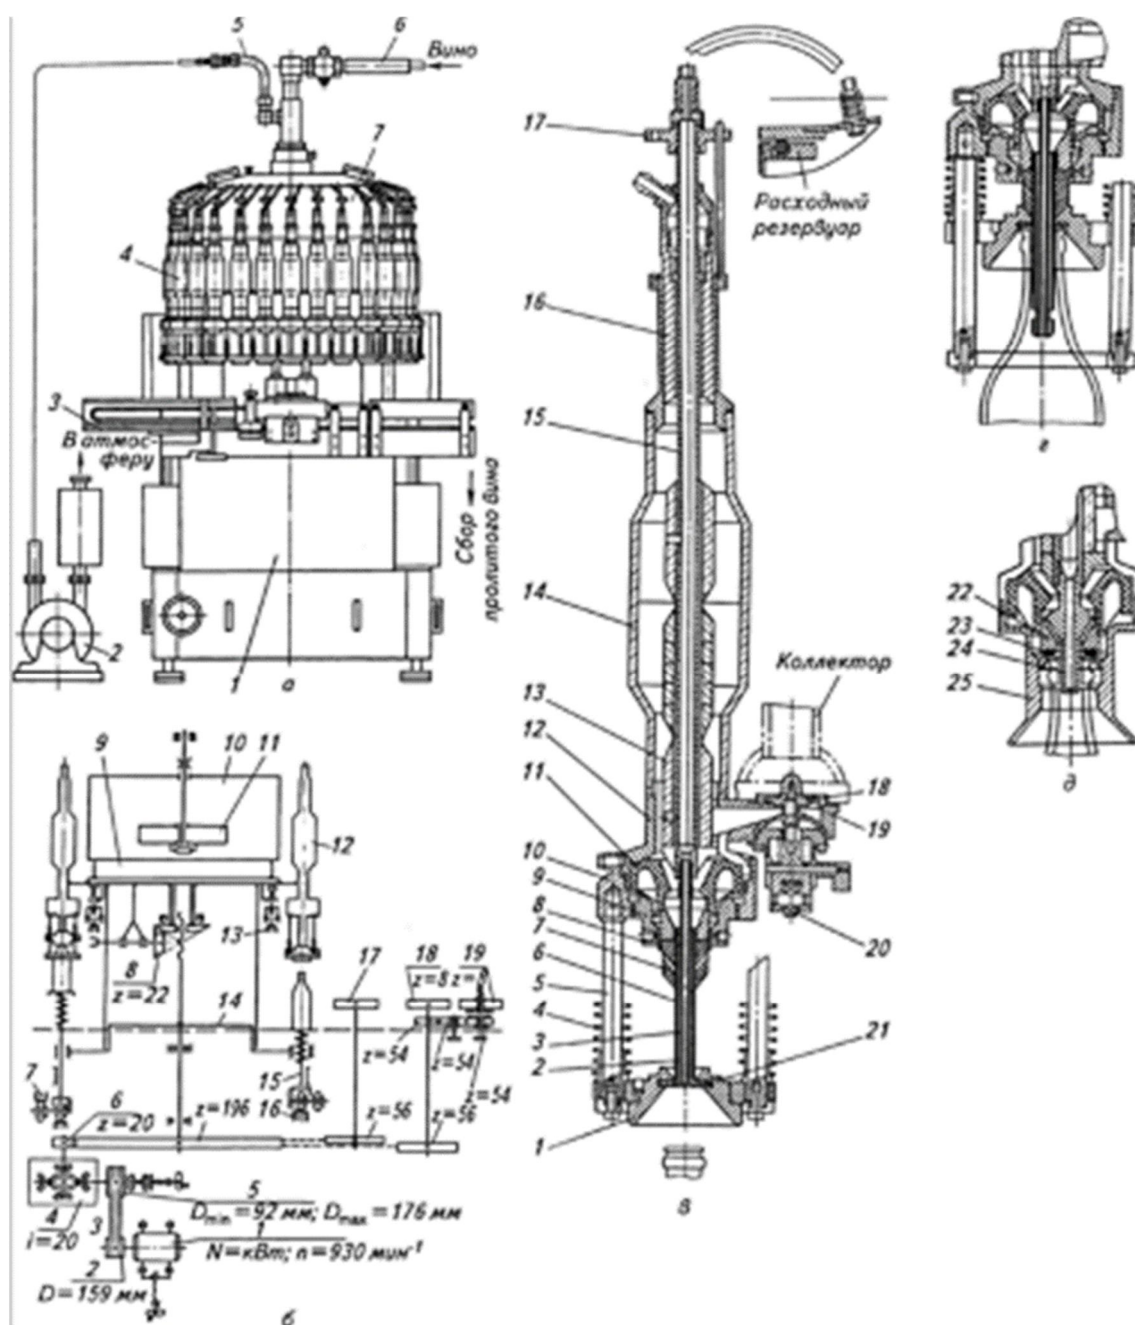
Дозувально-фасувальна машина ВРЦ: а - загальний вигляд: 1 - станина; 2 - вакуум-насос; 3 - конвеєр для пляшок; 4 - фасувальний пристрій; 5 - повітряна трубка; 6 - труба для подачі вина; 7 - витратний резервуар; 8 - кінематична схема: 1 - електродвигун; 2, 5 - шківи; 3 - клинопосова передача; 4 - редуктор; 6 - конвеєр; 7 - зворотний копір; 8 - механізм підйому витратного резервуара; 9 - колектор; 10 - видатковий резервуар; 11 - поплавок; 12 - фасувальний пристрій; 13, 16 - верхній і нижній копії; 14 - карусель; 15 - підйомний стіл; 17, 18 - розвантажувальна і завантажувальна зірочки; 19 -
